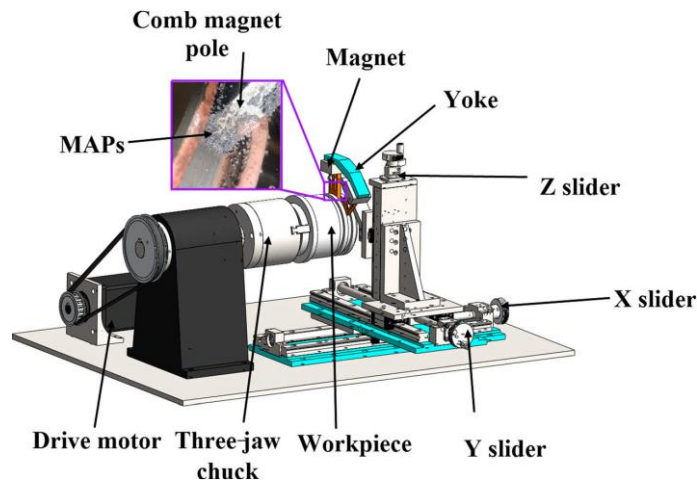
Зовнішній вигляд установки для оброблення кільцевої канавки
